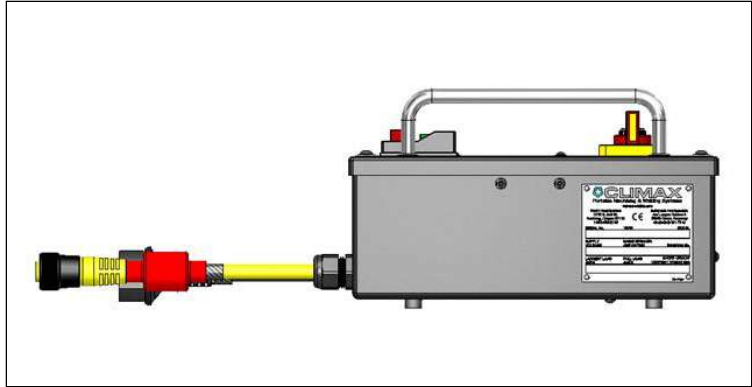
N/P 72918 UBICACIONES DE LA ETIQUETA LATERAL DEL CONTROLADOR WELDON SPINDLE 230V
